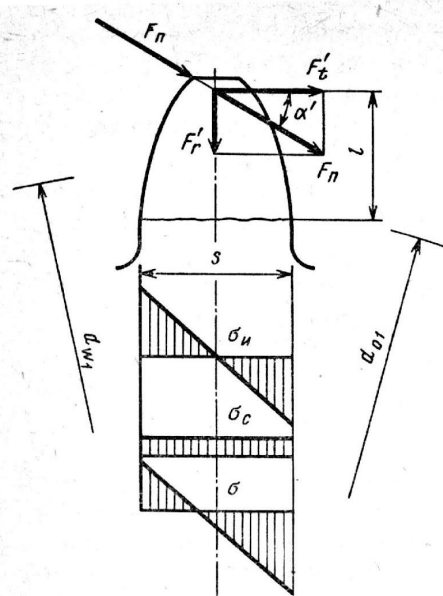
Расчетная схема нагружения зуба прямозубого цилиндрического колеса
